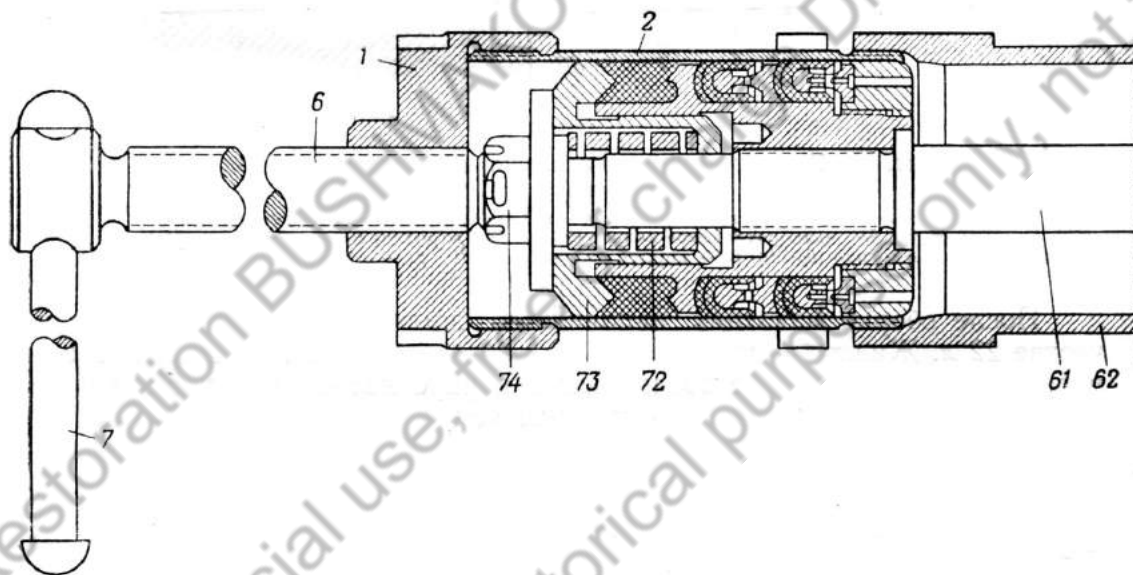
Втапливание поршня штока накатника при помощи прибора (сб. 42-18):
